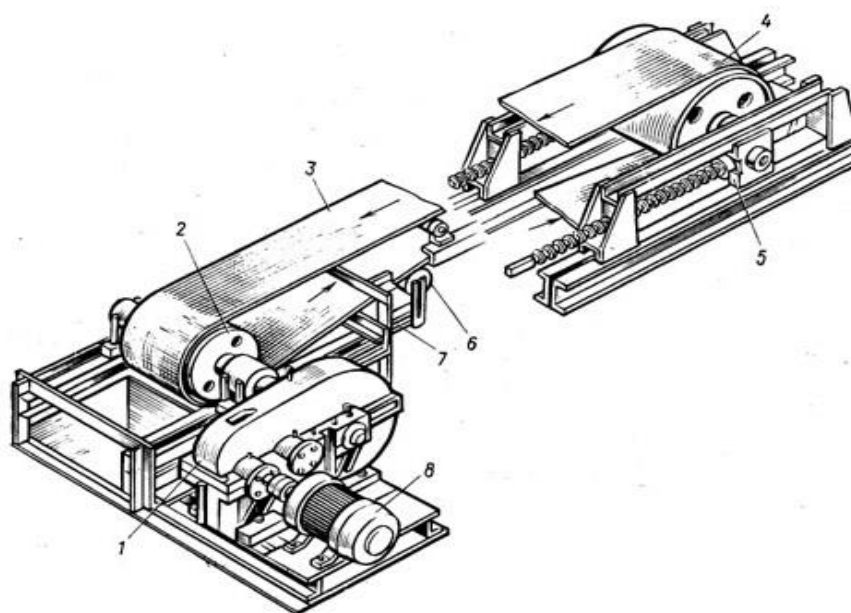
Ленточный конвейер: 1) редуктор; 2) приводной барабан; 3) прорезиненная лента; 4) обводной (натяжной) барабан; 5) натяжное устройство; 6) роlikовые опоры; 7) рама; 8) электродвигатель.
